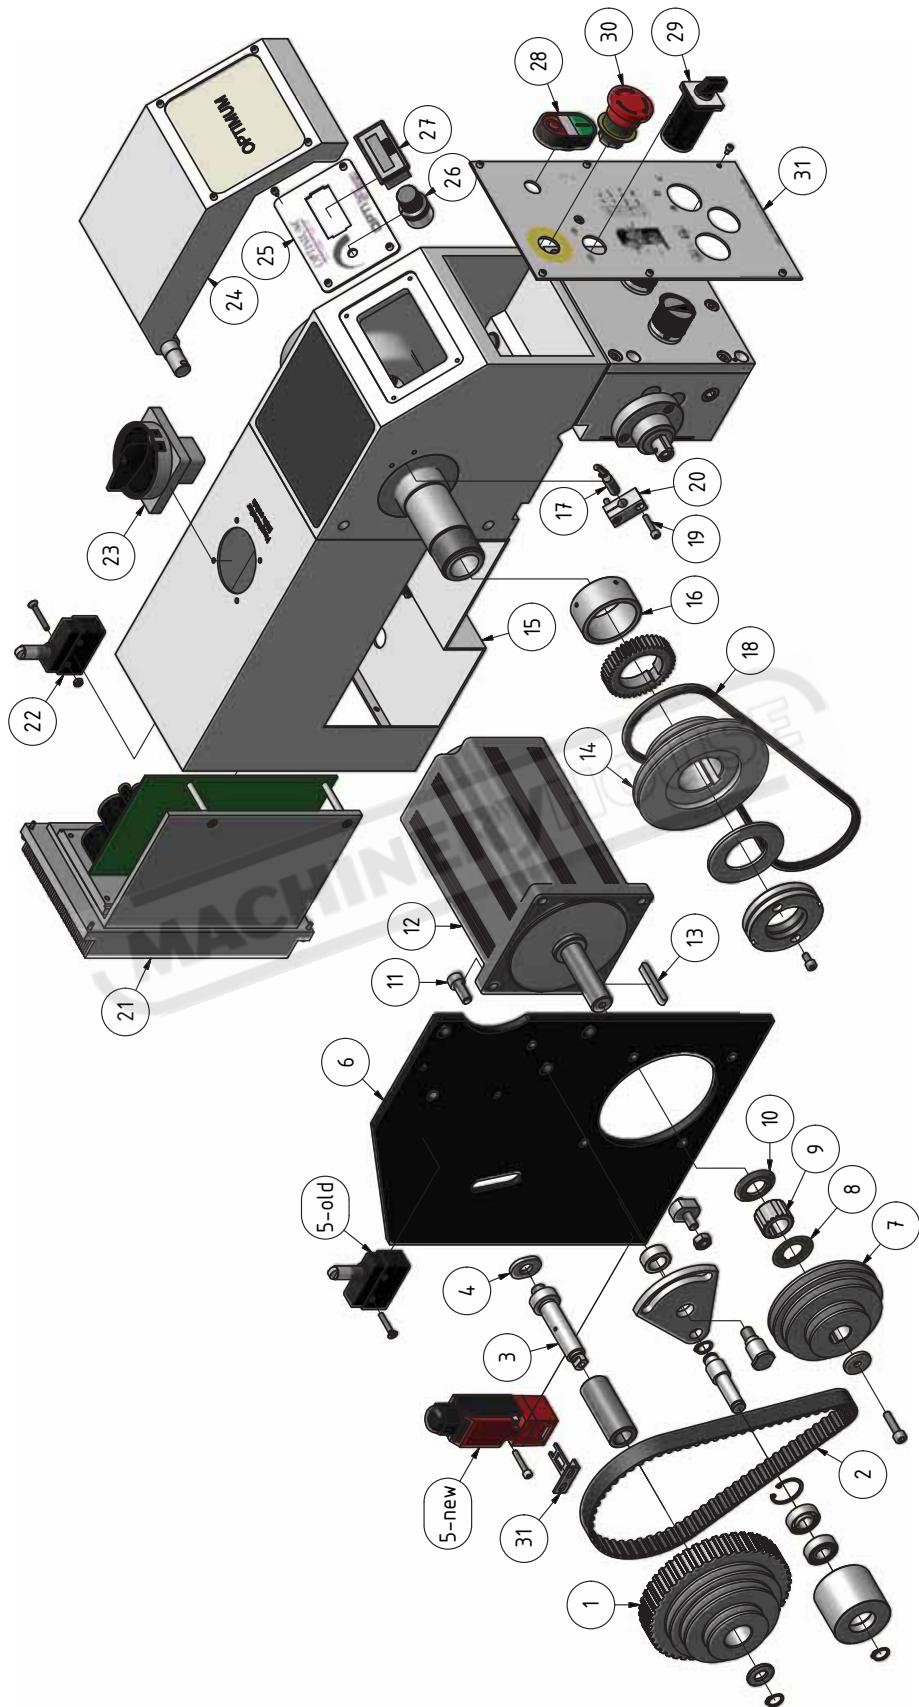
Spindelstock - Headstock TU 2506 V
